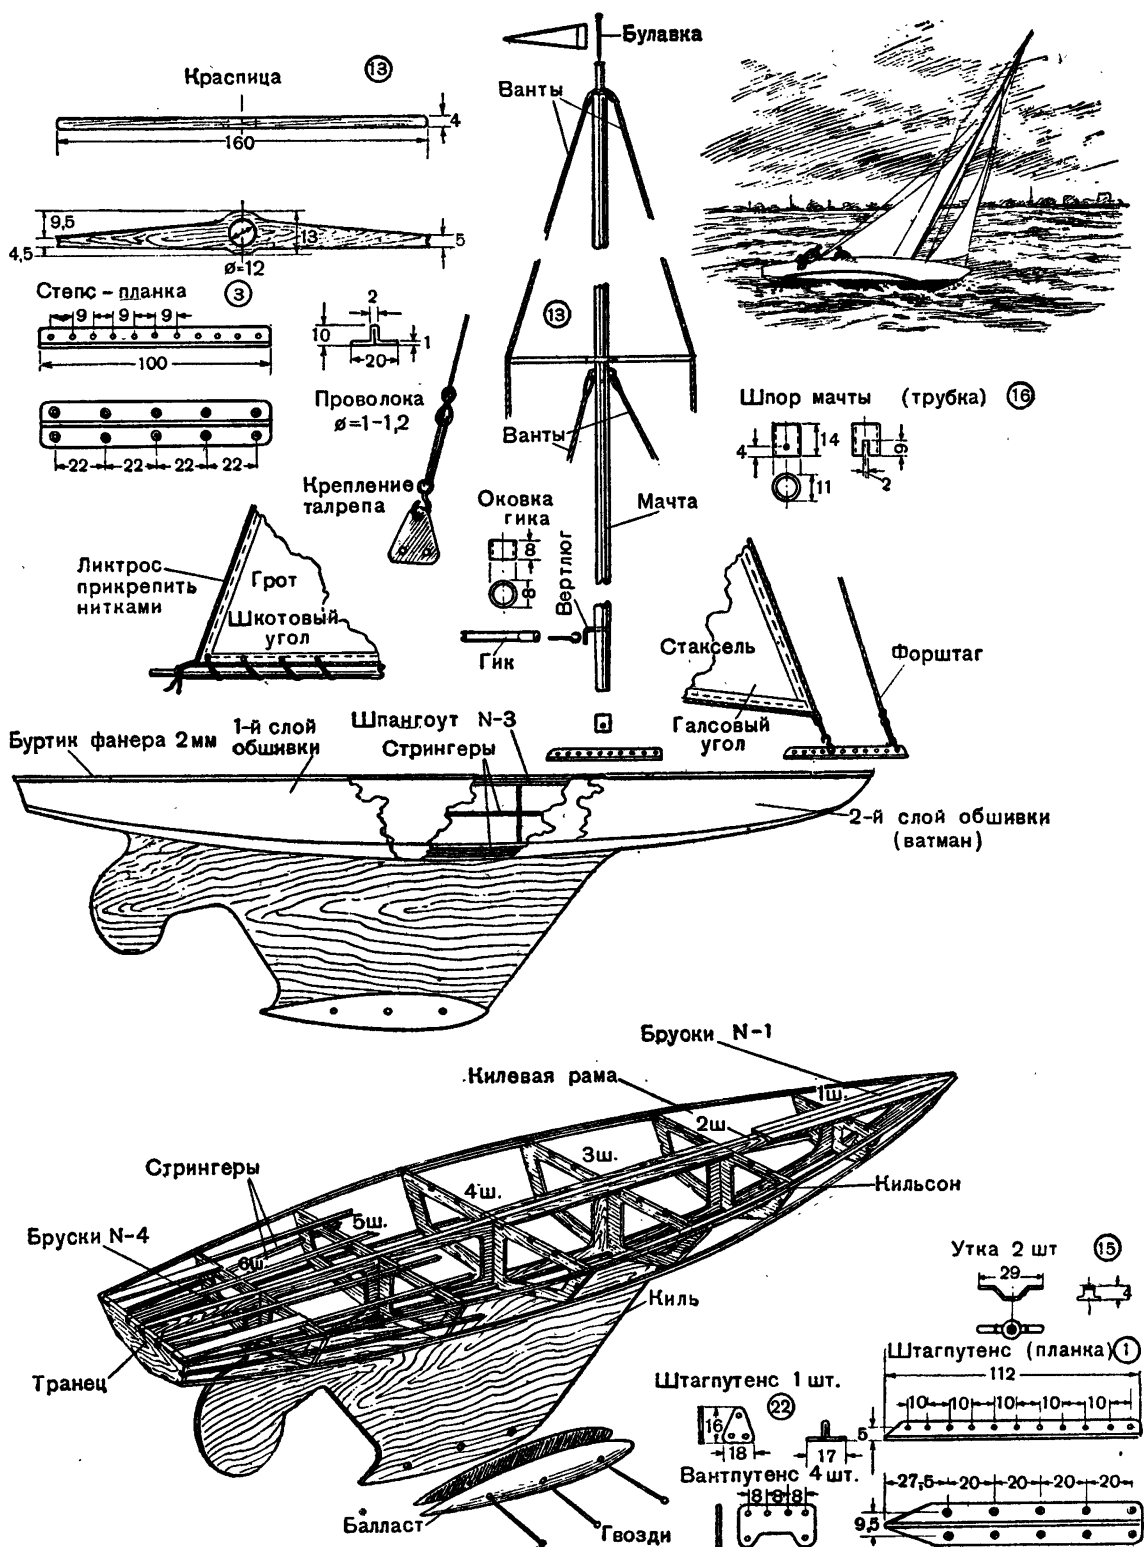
Конструктивный чертеж модели яхты класса «П».
